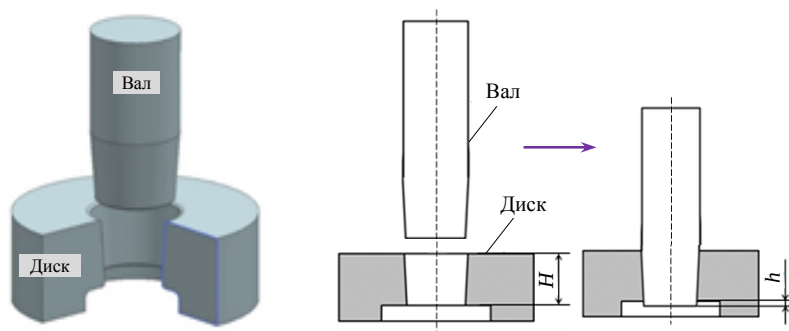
Общий вид образцов, имитирующих детали ГТД «диск + вал», и схема сварки давлением сплавов ЭК79 и ЭП975
